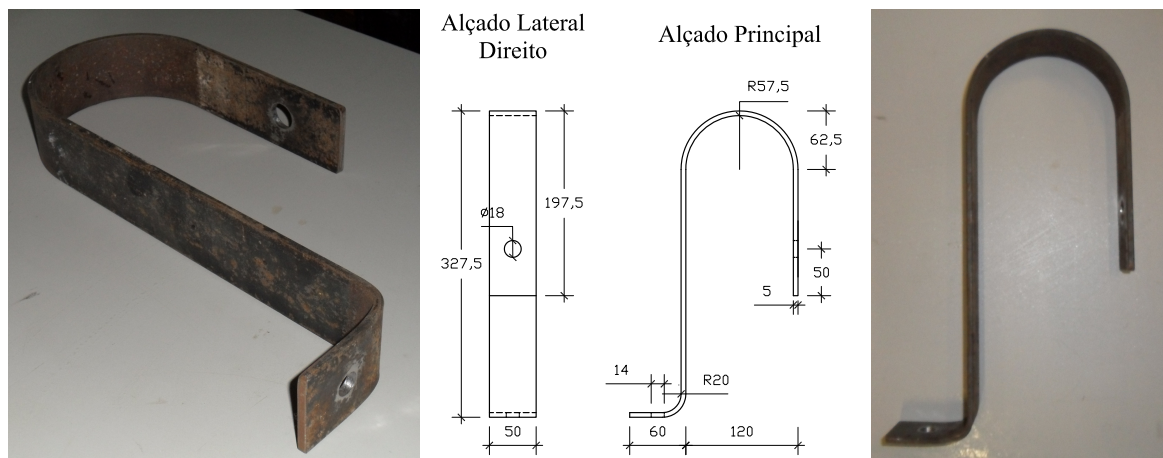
Vistas e dimensões do dispositivo DC 50x5 (mm)
